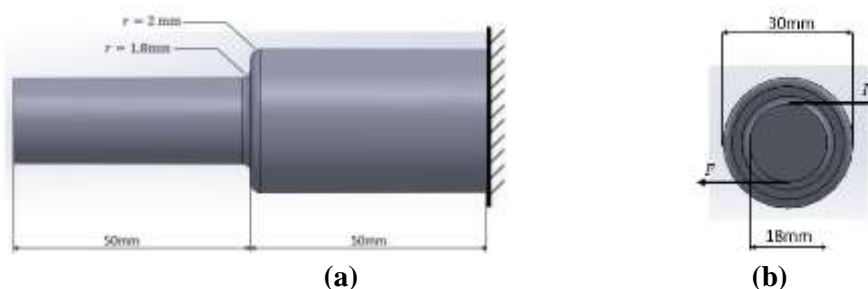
(a) Vista lateral do eixo rebaixado e adoçado, (b) Vista frontal do eixo rebaixado e adoçado sob torção
